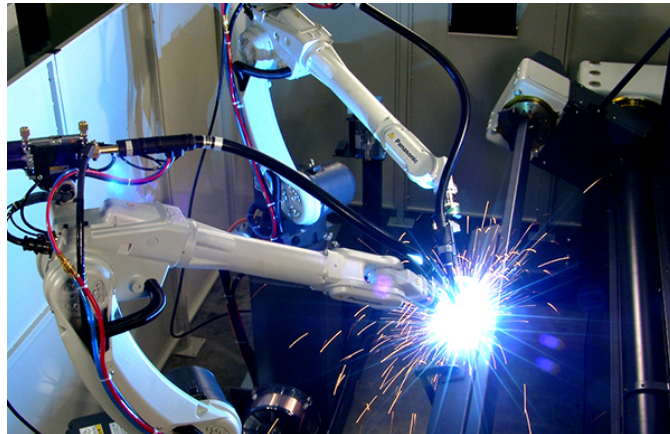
Robot industrial aplicando soldadura por arco [3].
